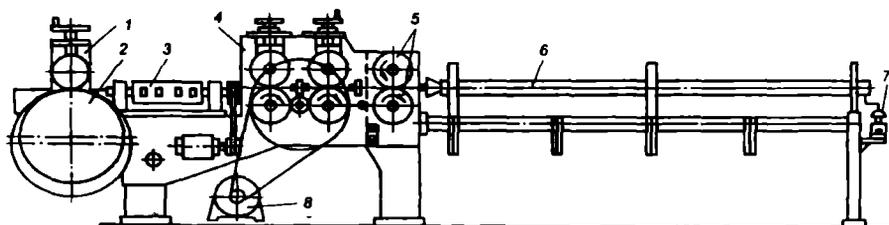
Станок непрерывного действия для правки, растяжения и резки арматуры:
